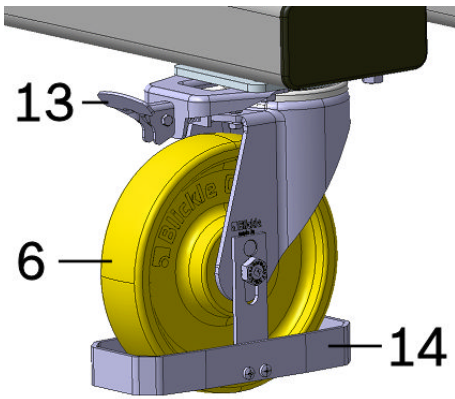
Самоустанавливающееся колесо, детальный вид
